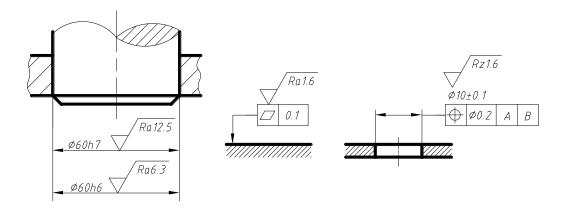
表面结构要求标注在尺寸线上 与 表面结构要求标注在形位公差框格的上方
